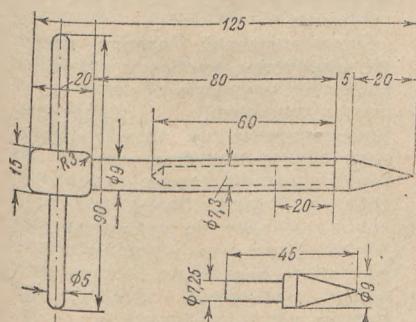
Приспособление для вставки резинового грибка в место прокола покрышки.
